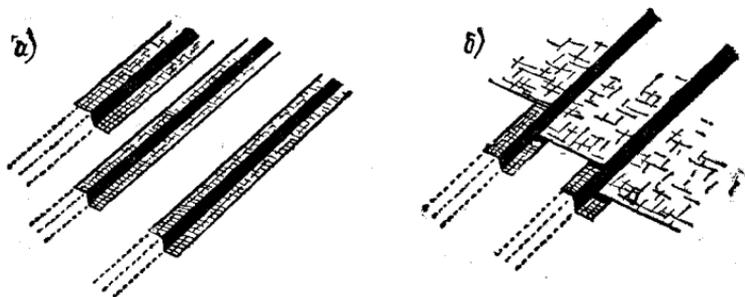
Оклейка корпуса с обшивкой кромка на кромку: а — оклейка выступающих кромок; б — оклейка поясьев между кромками.
